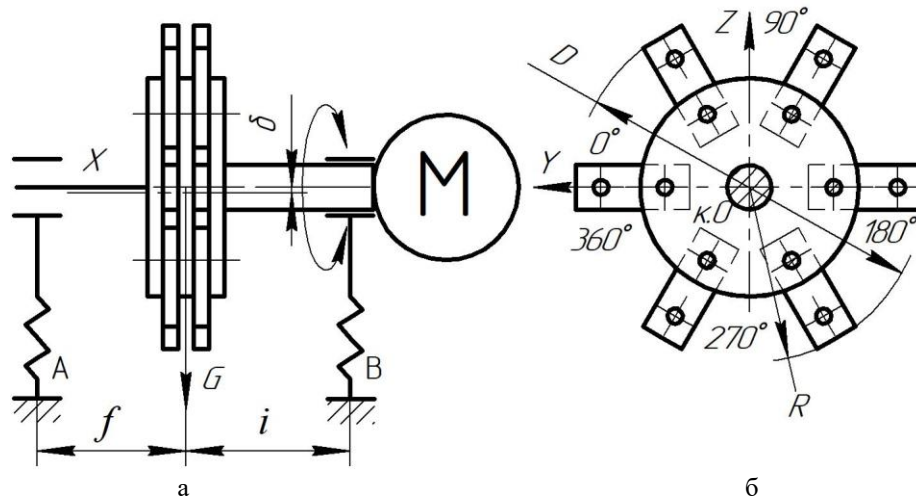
Розрахункова схема ротору молоткової дробарки: а – вид збоку; б – вид по осі ротора
